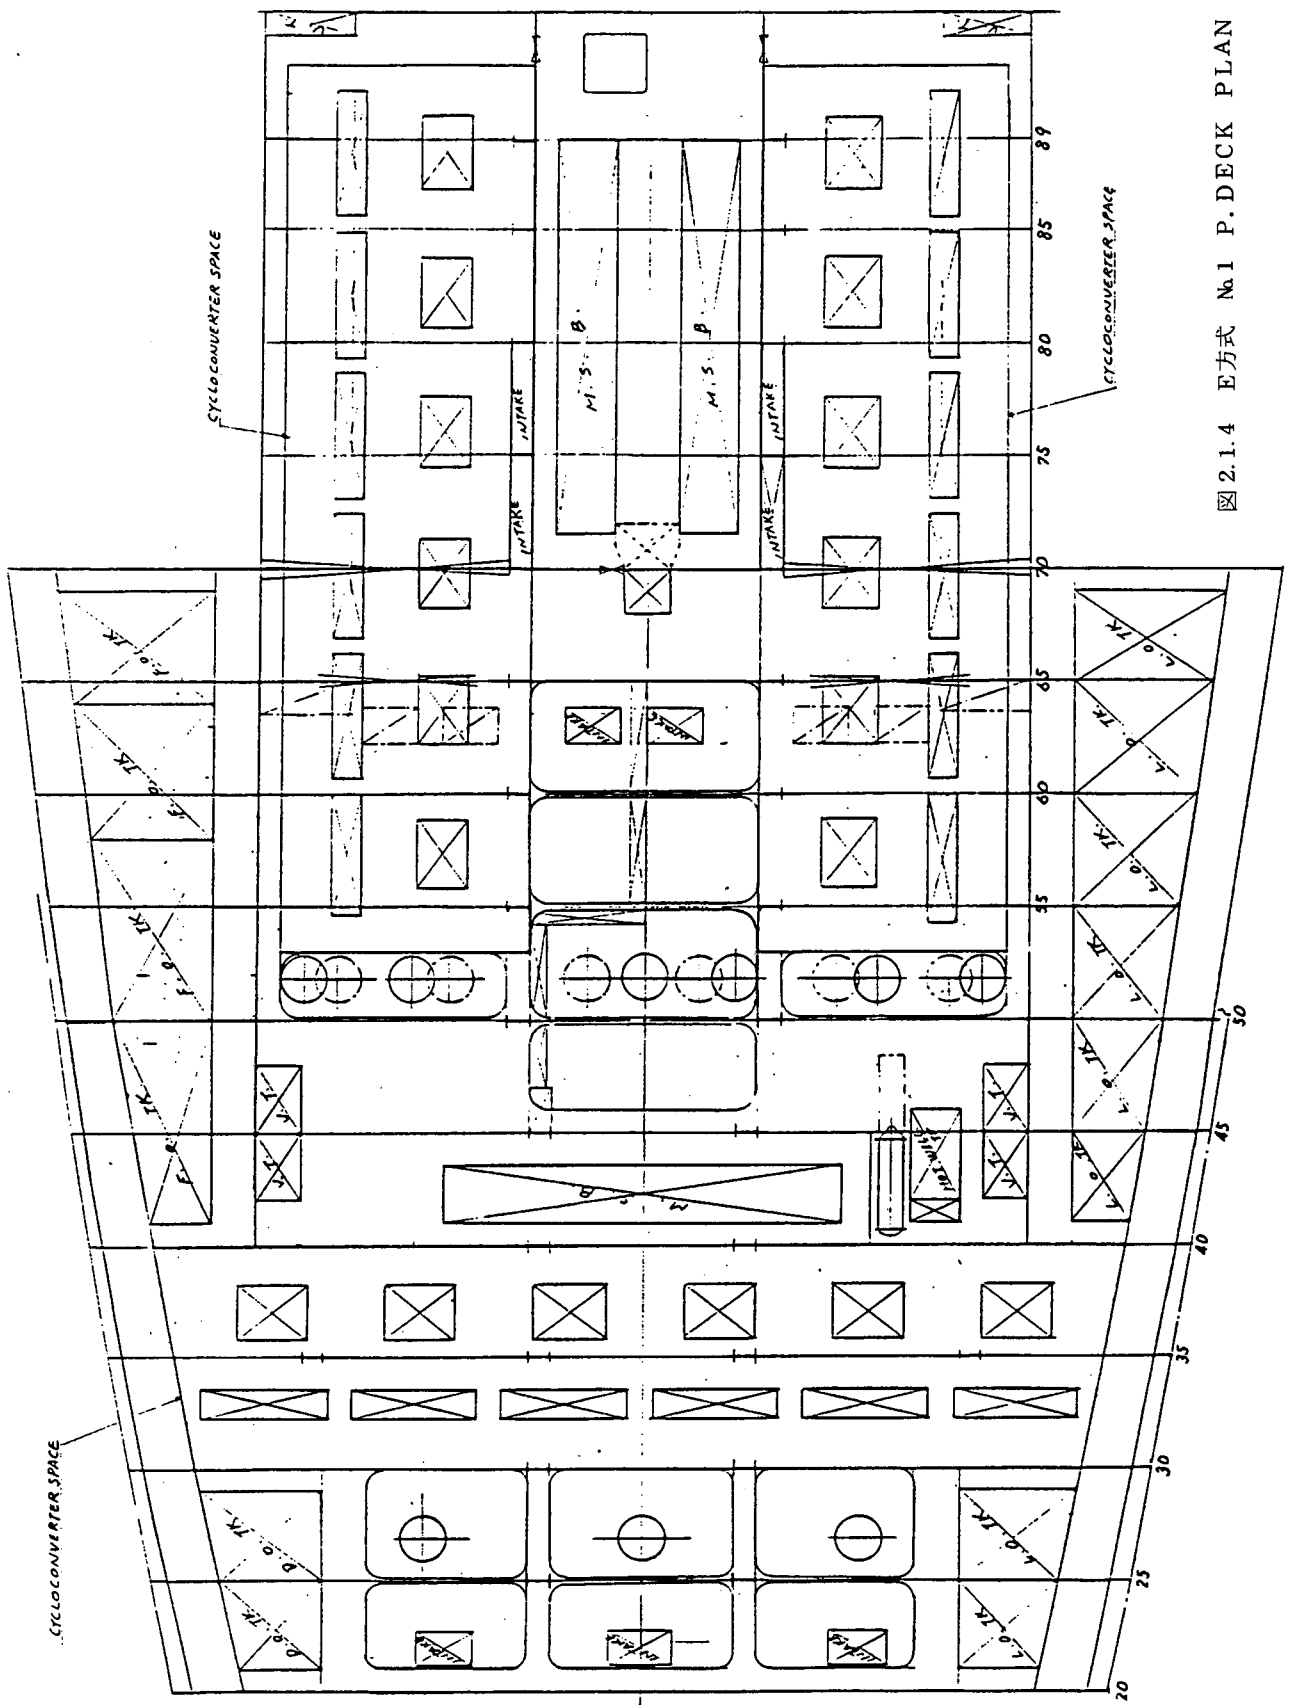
E 方式 No. 1 P. DECK PLAN
